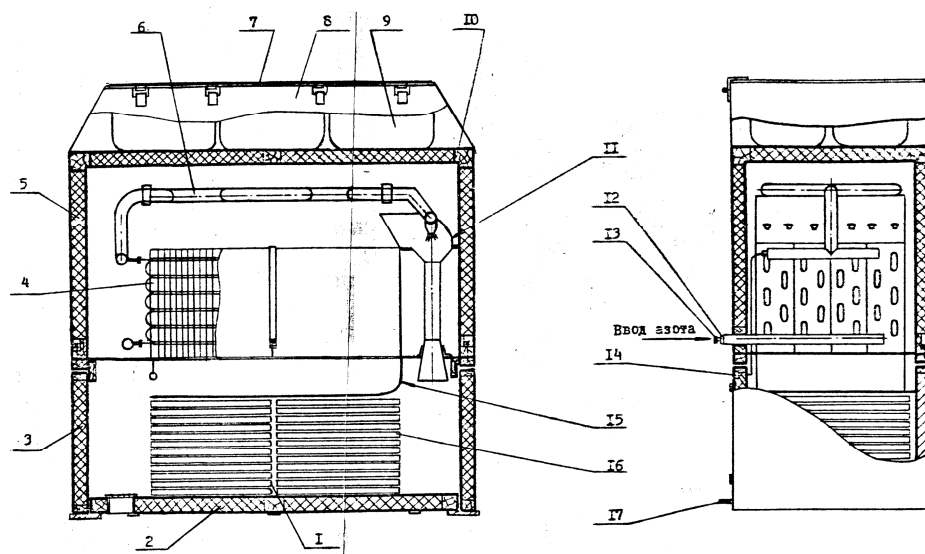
Холодильник: 1 – рама; 2 – корпус; 3 – крышка;
